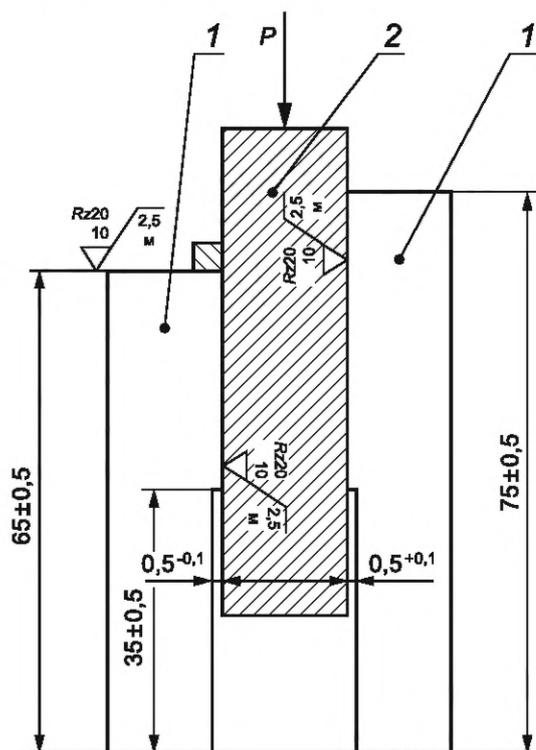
Размеры, форма и шероховатость образцов для испытаний на срез
